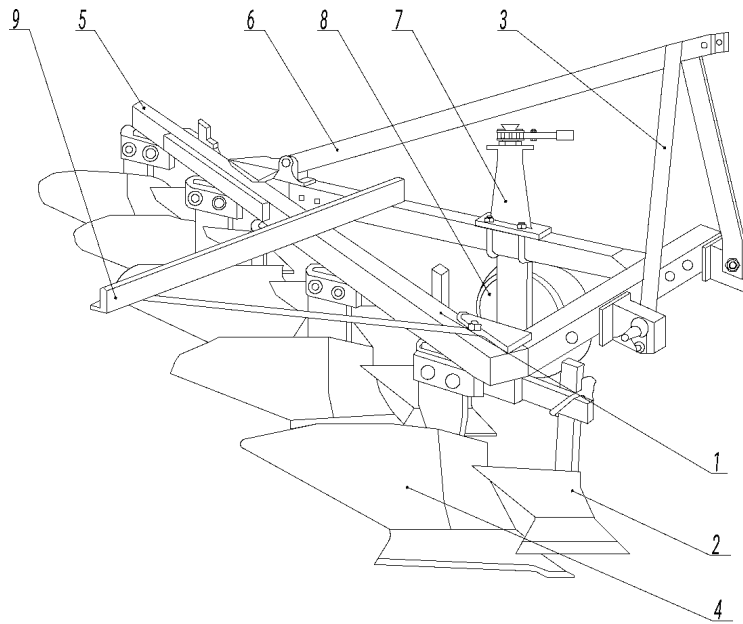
Плуг лемішний начіпний п'ятикорпусний ПЛН-5-35:
